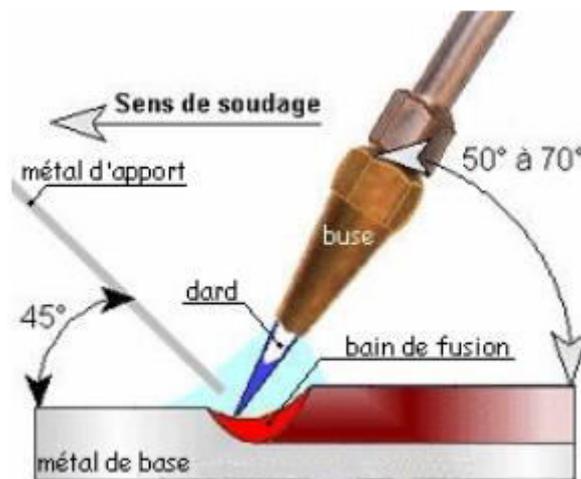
Schéma du soudage oxyacétylénique.
